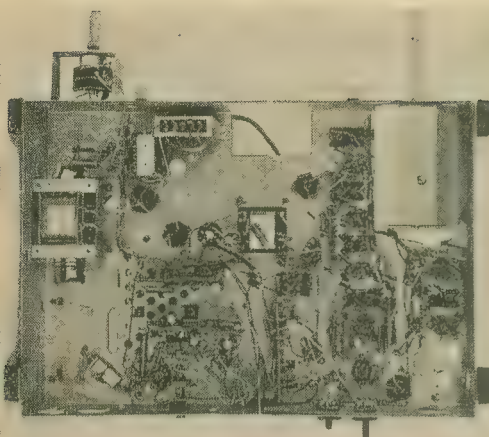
Untere Chassisansicht, tauchgelötete Baugruppen
